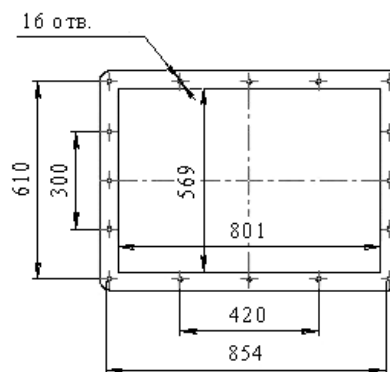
Вентиляторы ВПИ-PRU-1000. Присоединительные размеры
